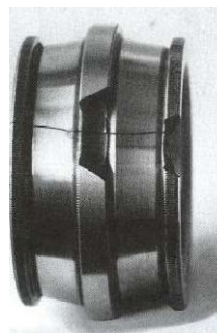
Fractura del aro interior de un rodamiento de rodillos a rótula. Uno de los rodillos ha sido extraído para permitir que el camino de rodadura en el lado izquierdo fuese examinado. El rodillo fue reinsertado con el martillo causando parte de la rotura de la pestaña central. Los impactos han sido transmitidos al camino opuesto a través de un rodillo, y parte de la pestaña también ha saltado. Al mismo tiempo el aro se ha fracturado transversalmente
